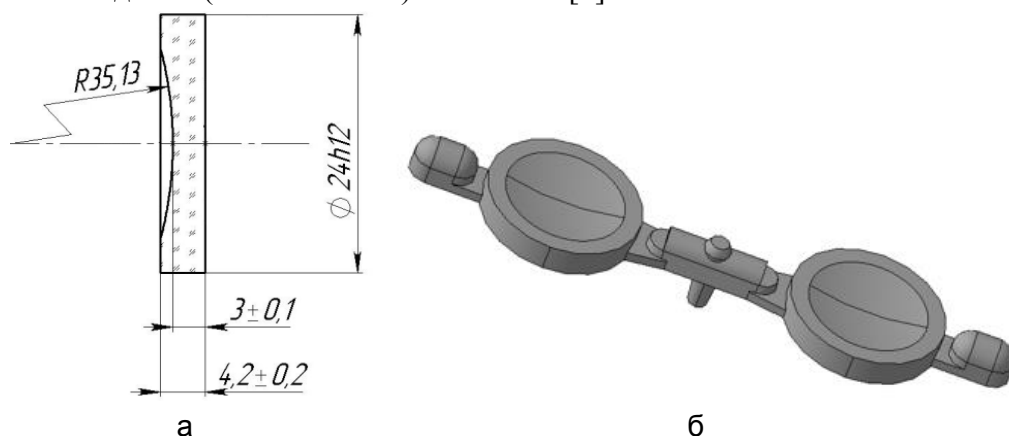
Эскиз линзы (а) и 3D-модель отливки для двугнездной литейной формы (б)
